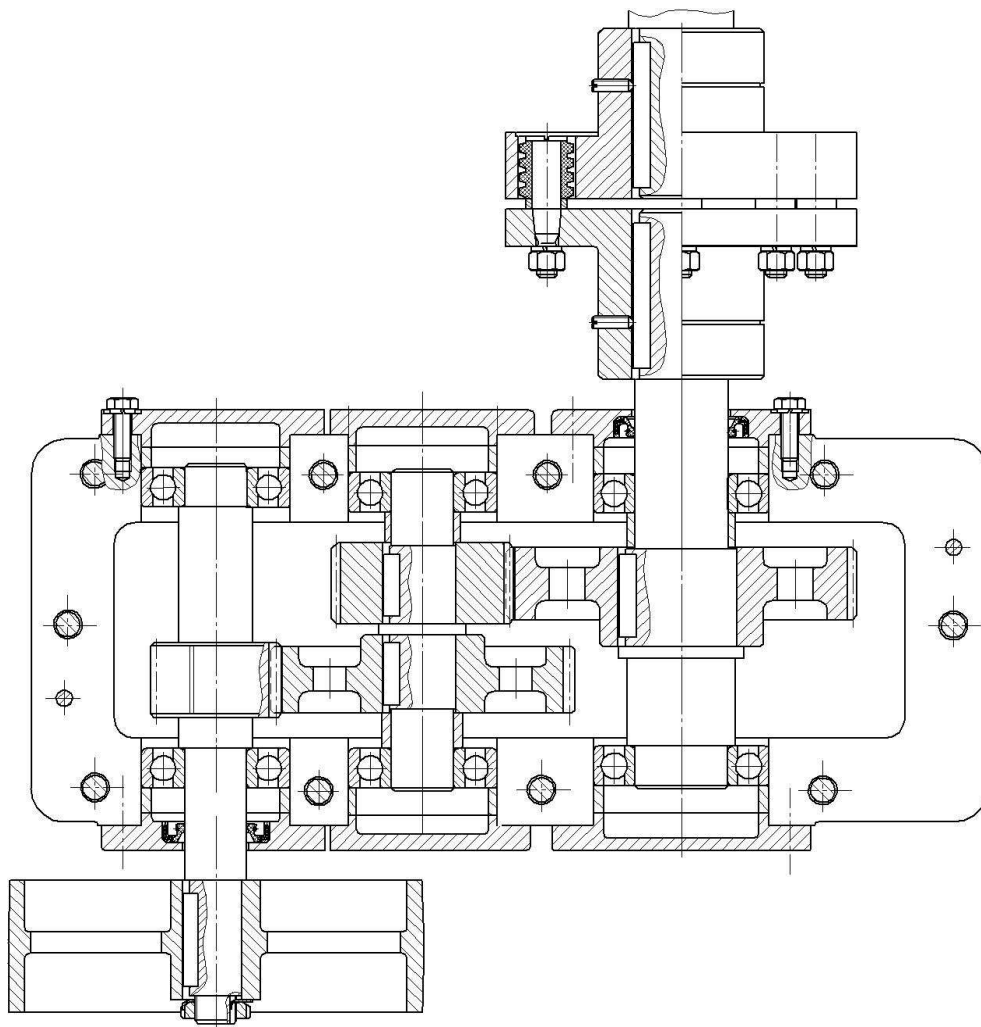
Упрощённый пример 1-го листа. Разрез редуктора по плоскости разъёма
